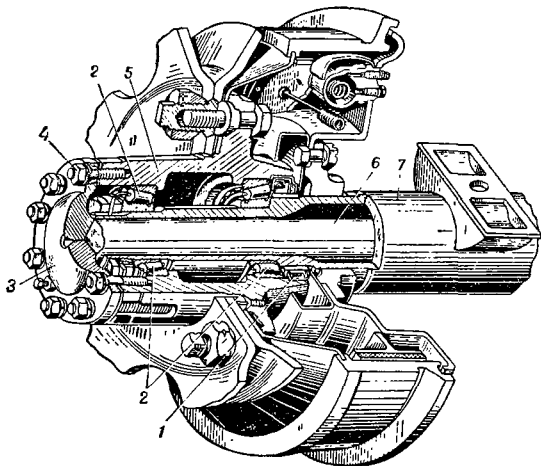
Фланцевое соединение приводного вала колеса с его ступицей (автомобиль ГАЗ-51).
